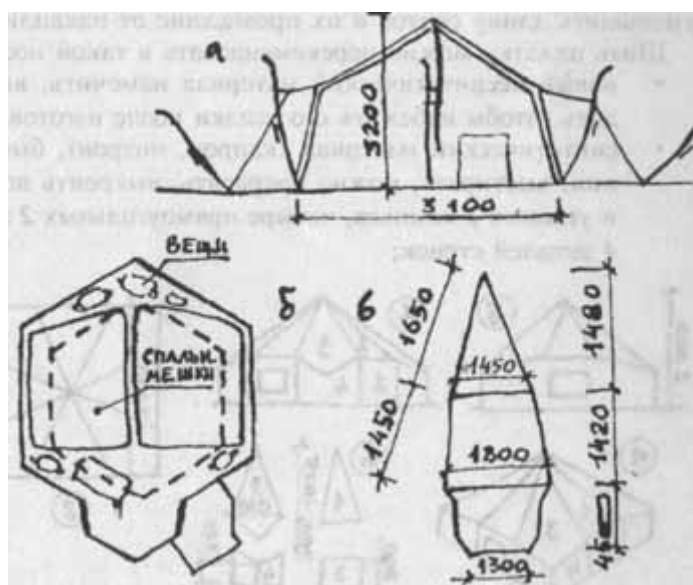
Шестигранная шатровая палатка: а) общий вид; б) вид сверху, размещение в палатке; в) раскрой клиньев.
